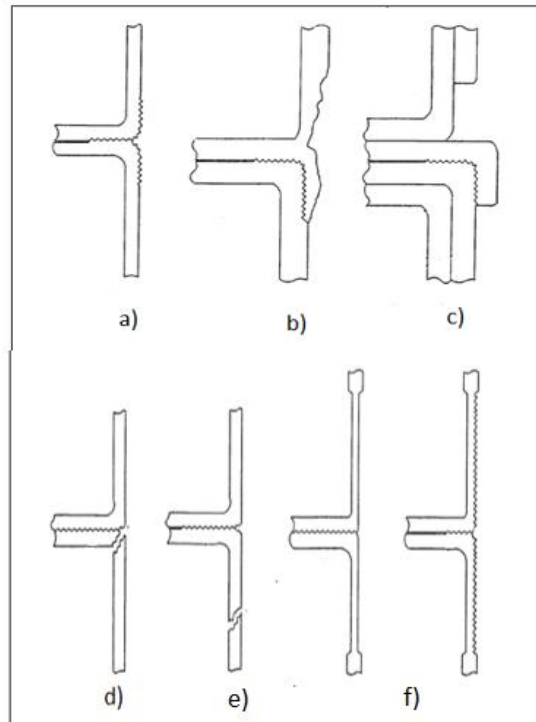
Representação das falhas do provete. a) Destaque da Soldadura; b) Falha coesiva do material; c) Rotura na camada selada (Delaminação); d) Falha de adesão da selagem (corresponde a uma má soldadura); e) Rotura de material indiferente á soldadura; f) Alongamento do material; [26]
